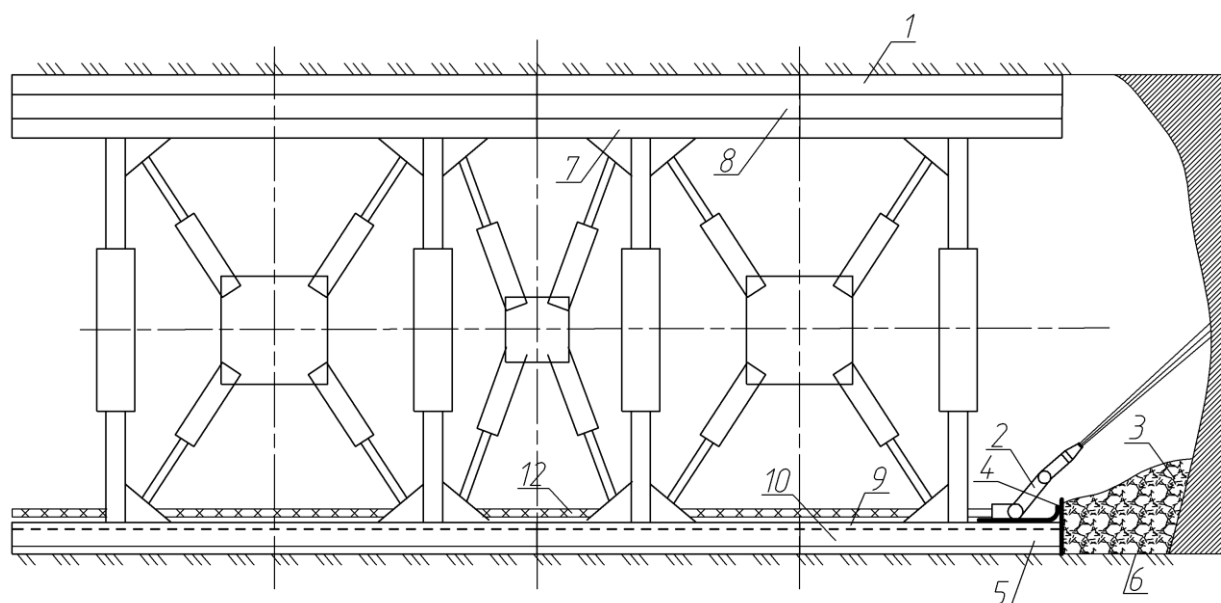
Проходческо-очистной гидравлический механизированный комплекс (вид сбоку)
